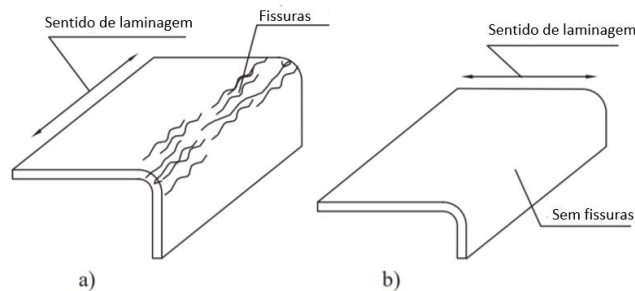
Relação entre quinagens com diferentes orientações de grão: a) quinagem paralela à laminagem; b) quinagem perpendicular à laminagem (adaptado de [35]).
